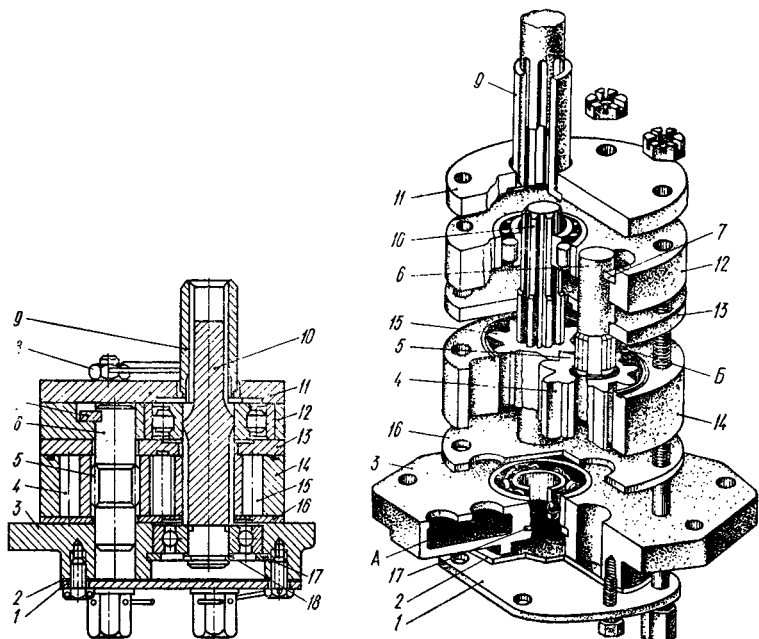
Насос гидросистемы коробки передач трактора К-701:
